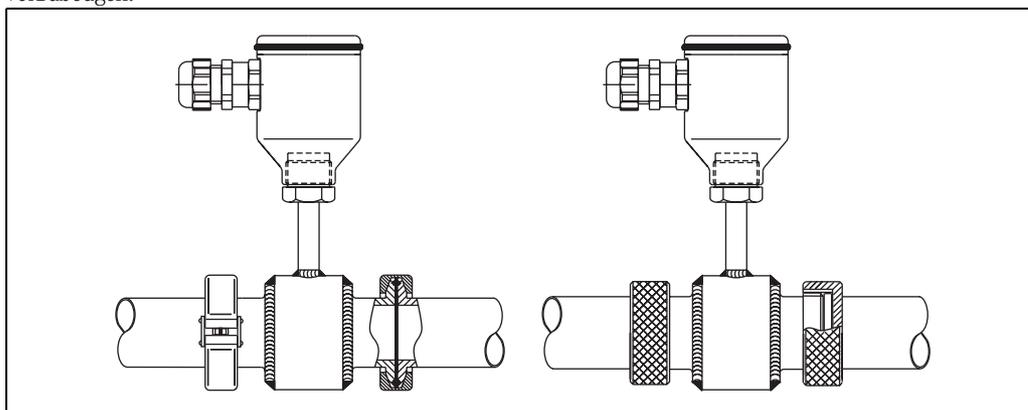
TR 46 mit Klemmanschlüssen (links) oder mit Einschraubgewinden (DIN 11851 oder DIN 11864-1-A) (rechts).
